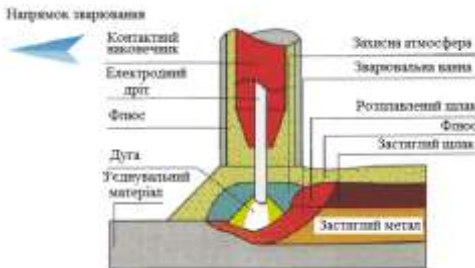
Схема автоматичного зварювання під шаром флюсу
